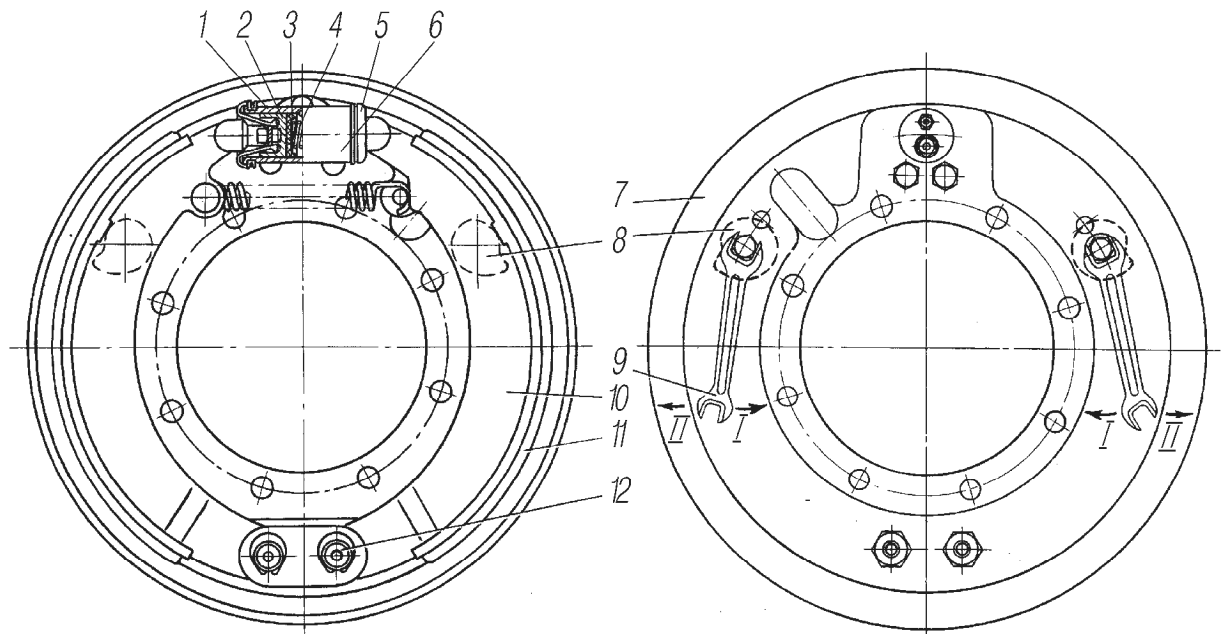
Механизм тормозной рабочий с двухполостным цилиндром:
